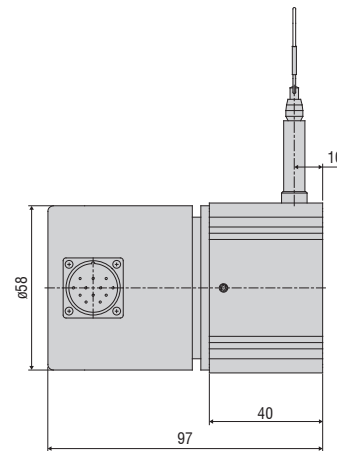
Maßzeichnung WDS- ... - P60 - SR - SSI
